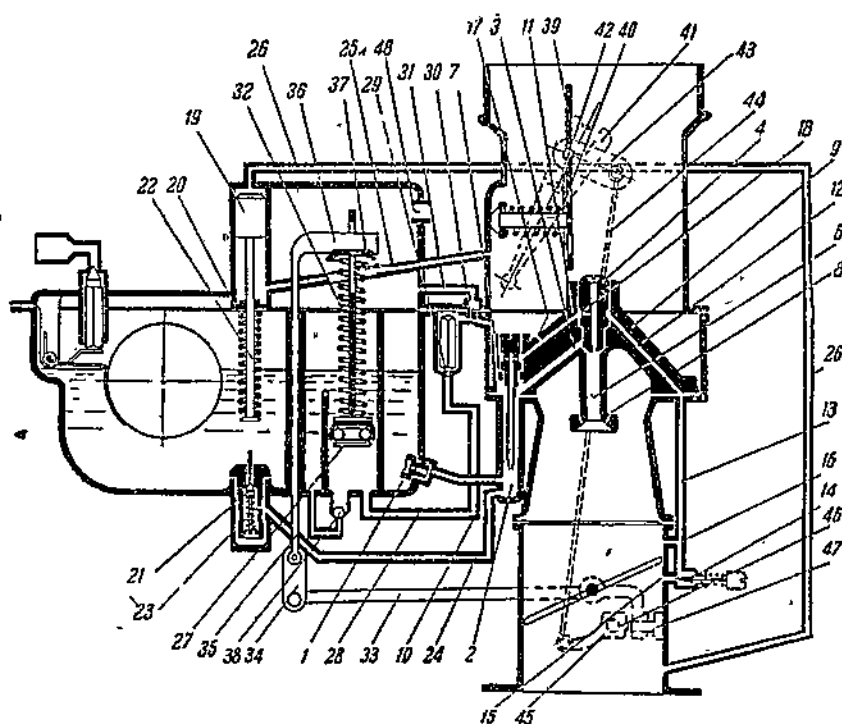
Развёрнутая схема карбюратора Форд автомобиля Форд 2G8T
